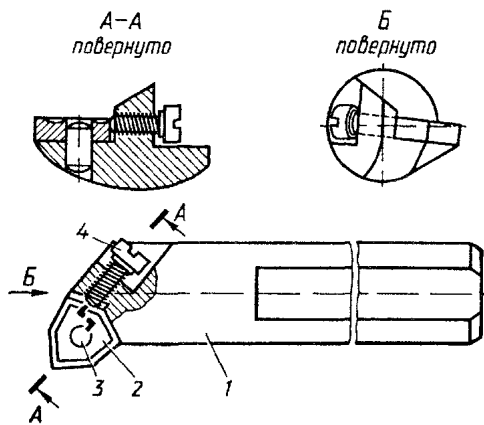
Розточувальний різець з механічним кріпленням трилезової попереточуваної твердосплавної пластинки: 1- державка; 2 -твердосплавна пластинка; 3 - штифт; 4 - гвинт
